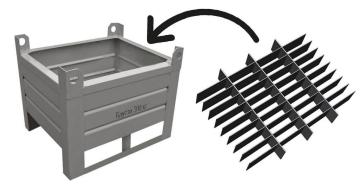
Металлическая сетчатая тара ТМП-24, используемая для хранения и передачи заготовок и корпусов рабочих секций
